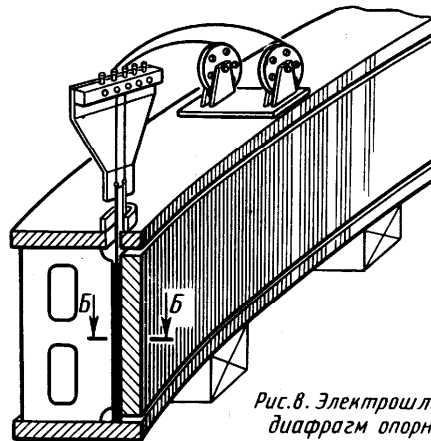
Электрошлаковая сварка внутренних диафрагм опорного кольца конвертора
